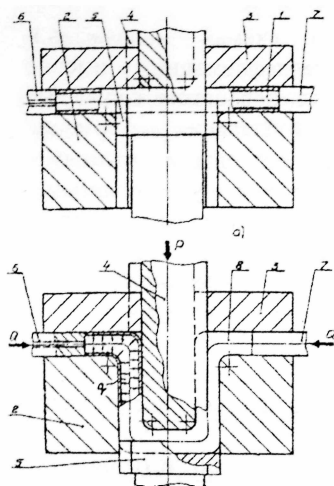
Схема деформирования трубной заготовки в крутоизогнутый Γ -образный полуфабрикат:
